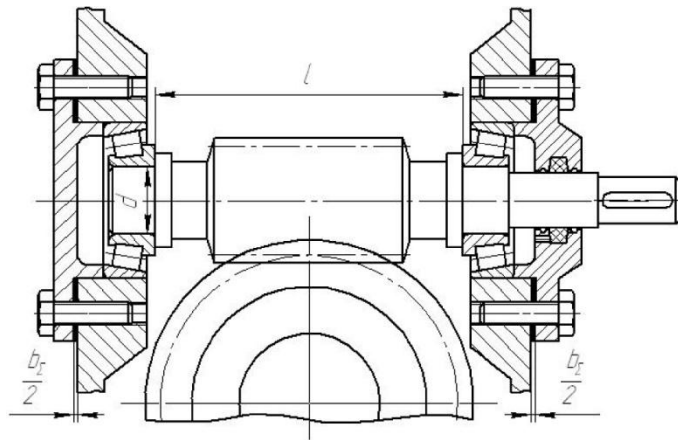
Вузол вала черв'яка з підшипниками, установленими «врозпір»
